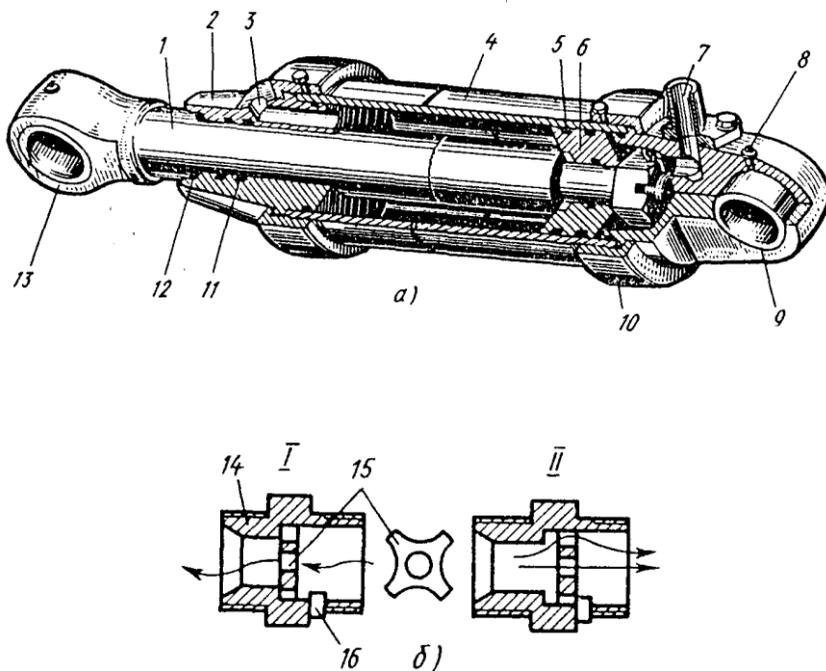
Общий вид силового гидроцилиндра объёмного гидропривода
